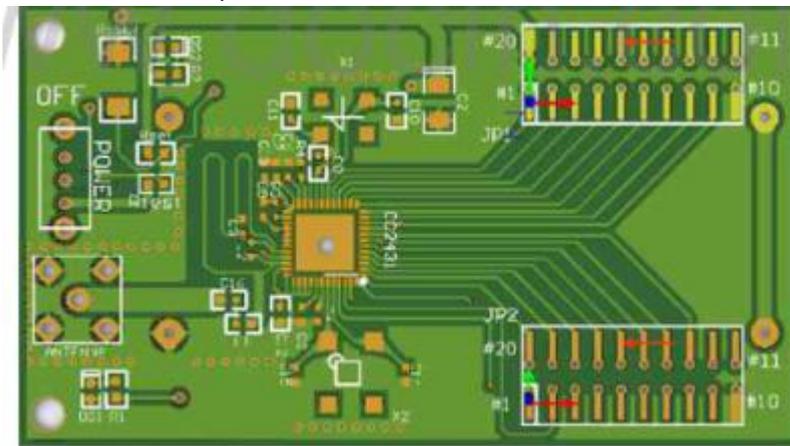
DS210A 型 CC2430/1 节点板 PCB 图
